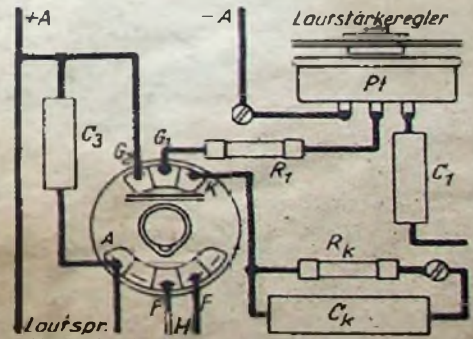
Verdrahtungsplan einer Endstufe mit EL 1, EL 12
